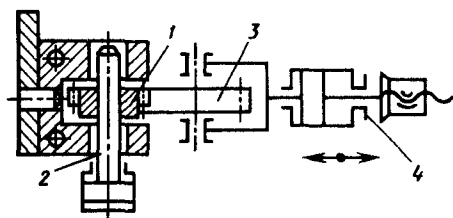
Схема зубокалибрования одним накатником с радиальным движением подачи инструмента:
